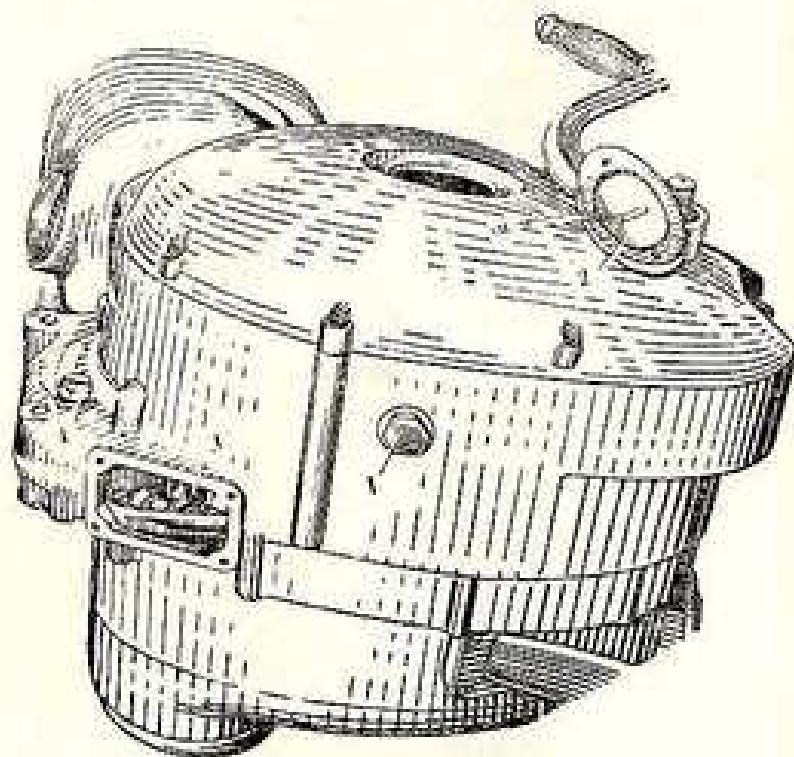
ВИД ДВИГАТЕЛЯ СНИЗУ:
